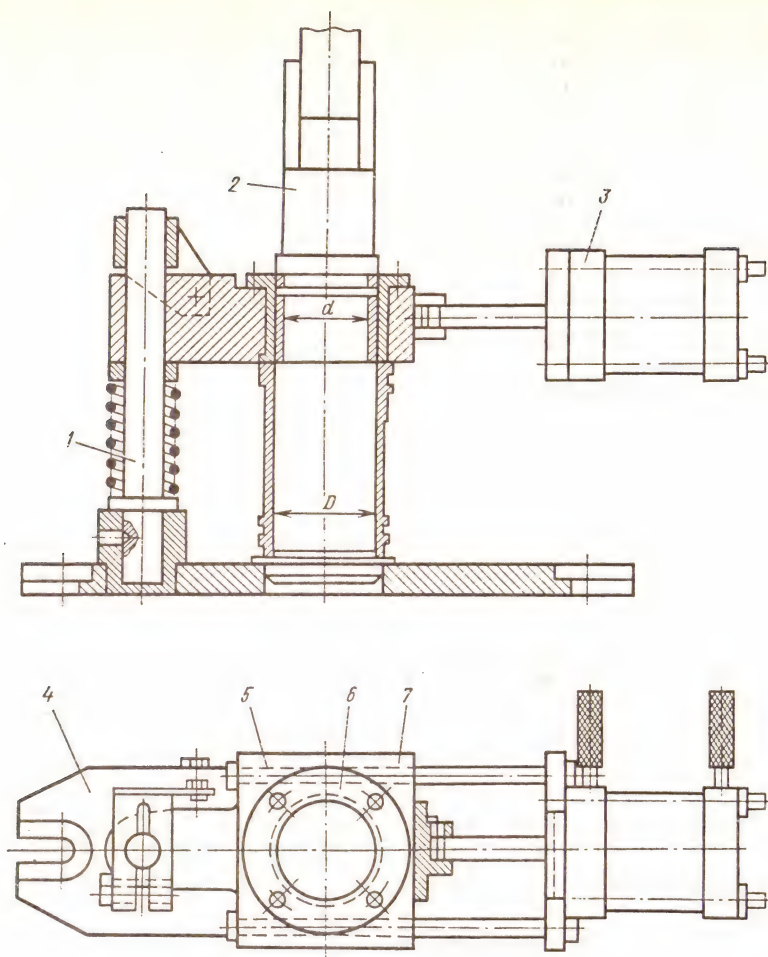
Приспособление для совмещения операций свертывания и запрессовки пластины в гильзу цилиндров:
